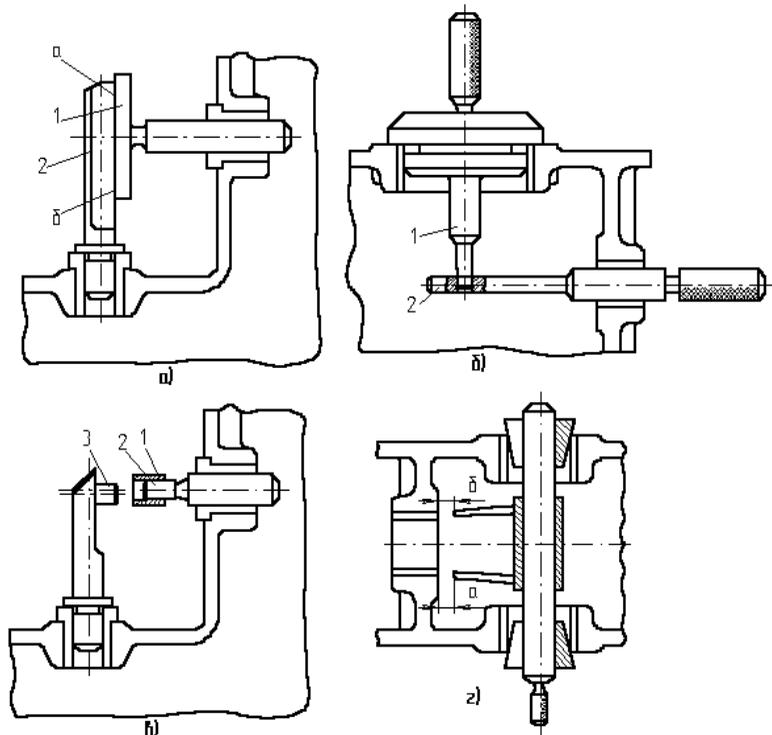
Схемы контроля положения осей отверстий при сборке конических передач:
